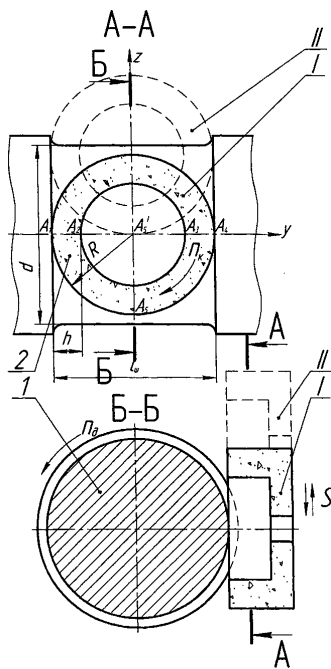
Технологічна схема шліфування шийки вала торцем круга.
